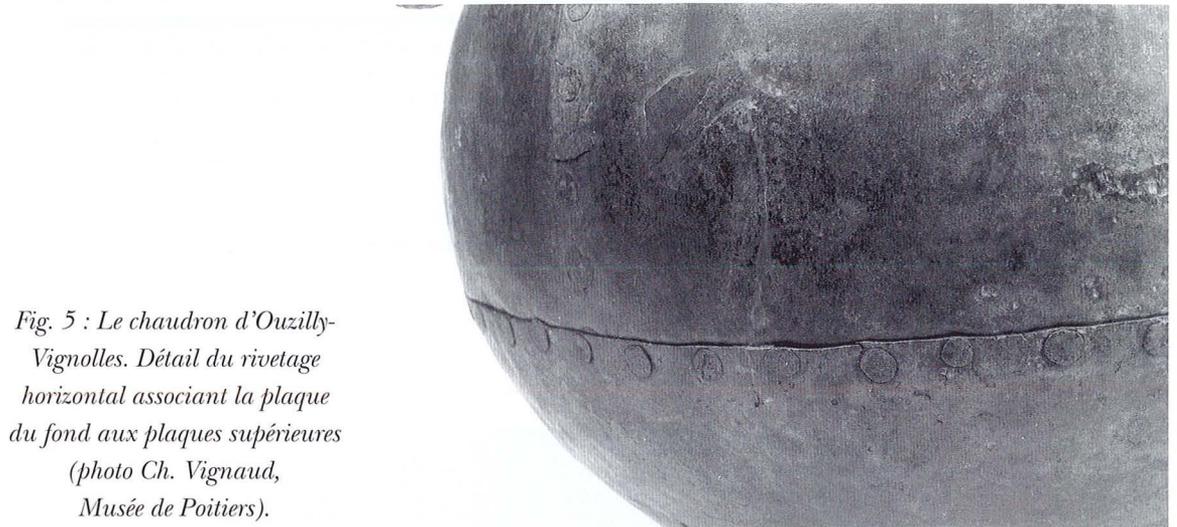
Le chaudron d'Ouzilly-Vignolles. Détail du rivetage horizontal associant la plaque du fond aux plaques supérieures (photo Ch. Vignaud, Musée de Poitiers).
